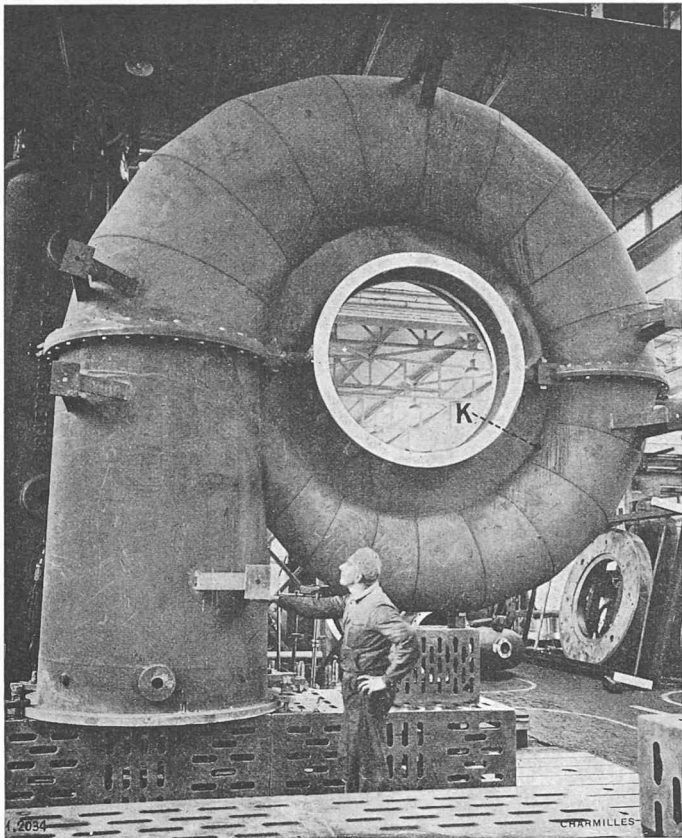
Bâche en tôle soudée selon la construction brevetée Piguet-Charmillles
